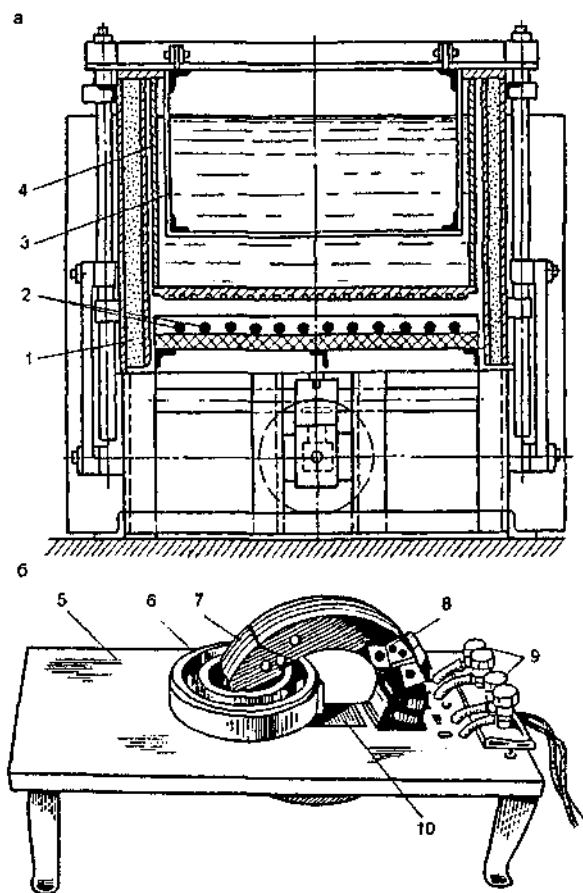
Приспособления для нагрева подшипников качения при посадке на вал электрической машины
